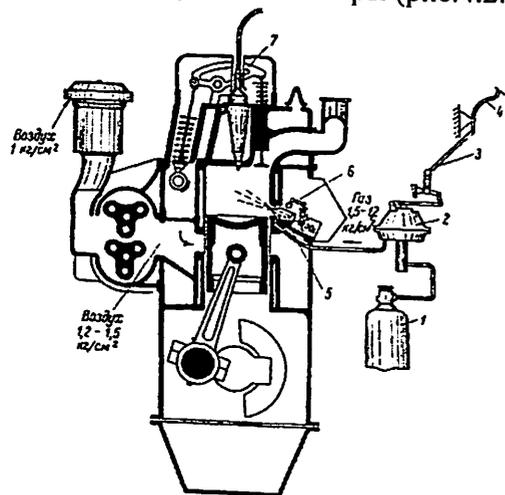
Схема газового двигателя на базе ЯАЗ-204
